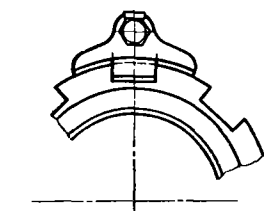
Стопорение кольцевой гайки привертной пластинкой
